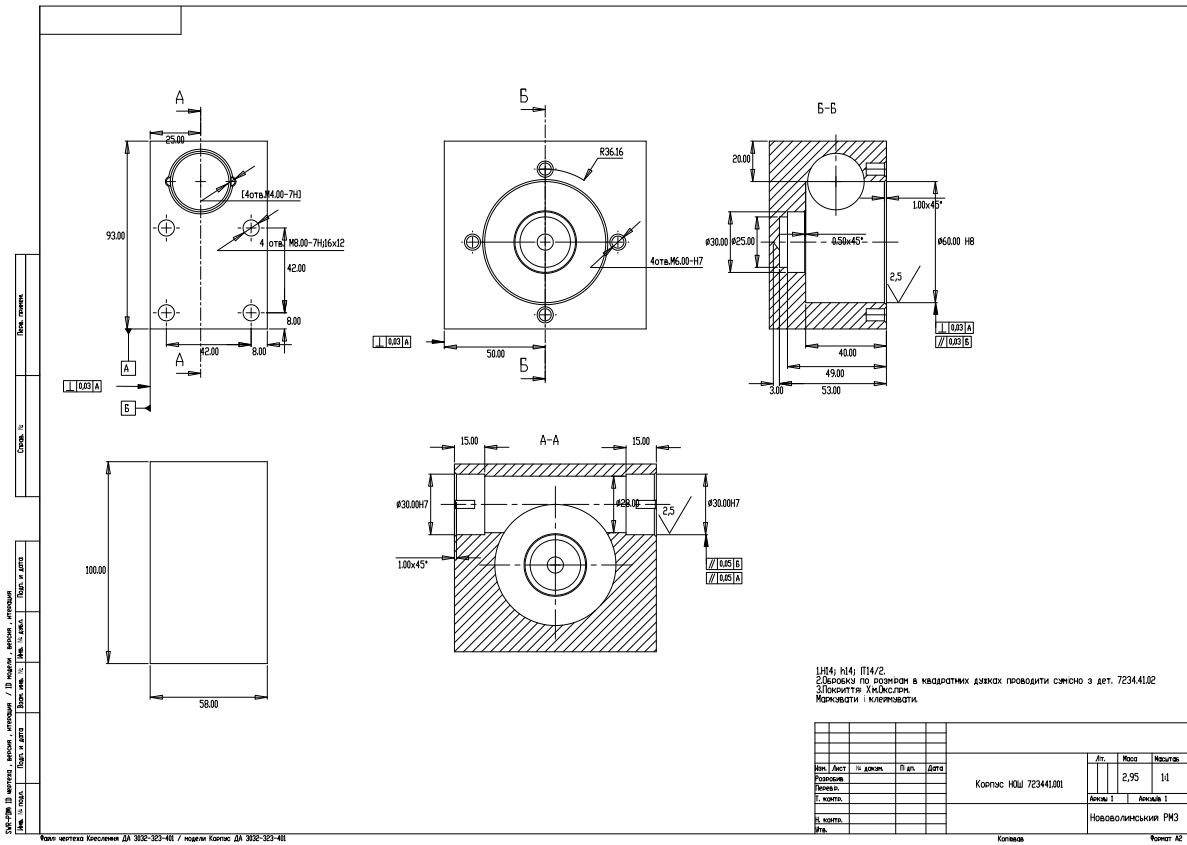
Робочий кресленник деталі «Корпус НОШ 7234.41.001»
